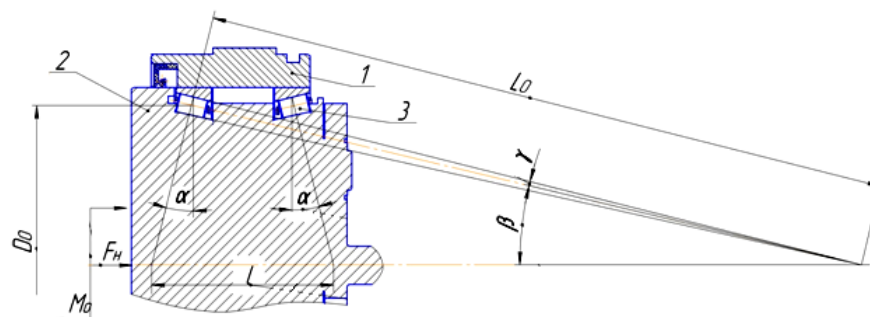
Вариант компоновки совмещенных опор качения планетарно-цевочного редуктора типа ПЦР 3-36(6): 1 – корпус; 2 – водило; 3 – радиально-упорная совмещенная опора качения; α – угол контакта конического ролика; M_o – опрокидывающий момент; F_H – внешняя осевая сила; L – расстояние между точками приложения опорных реакций; L_o – длина среднего конусного расстояния ролика; D_o – диаметр центров комплекта роликов; β – номинальный угол контакта ролика; γ – угол конусности ролика
